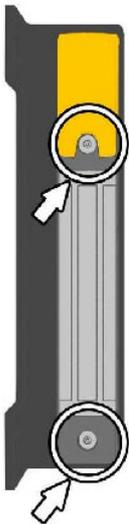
Prozesszuhaltung auf Montageplatte anbringen und Schrauben M6 x 25 mm Torx festziehen.
